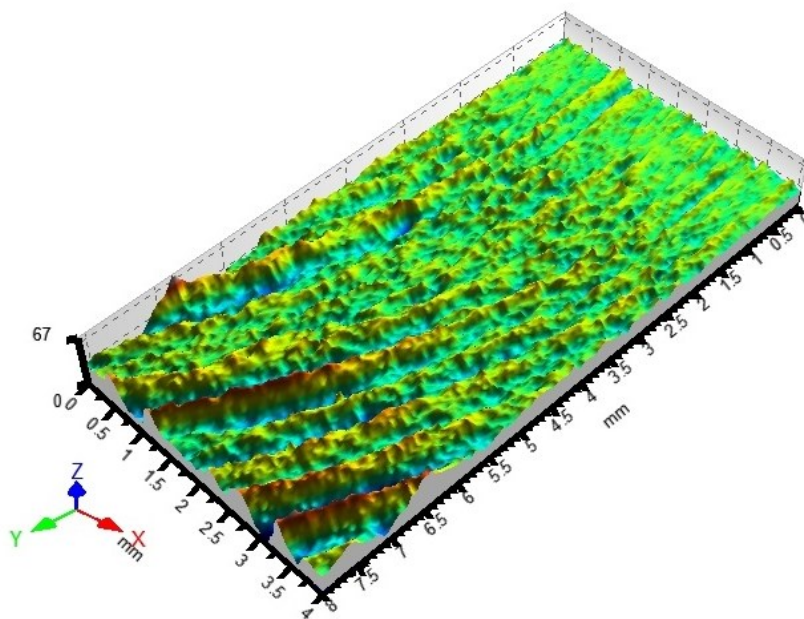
3D pohled snímaného povrchu vzorku Q1 po odstranění tvaru
